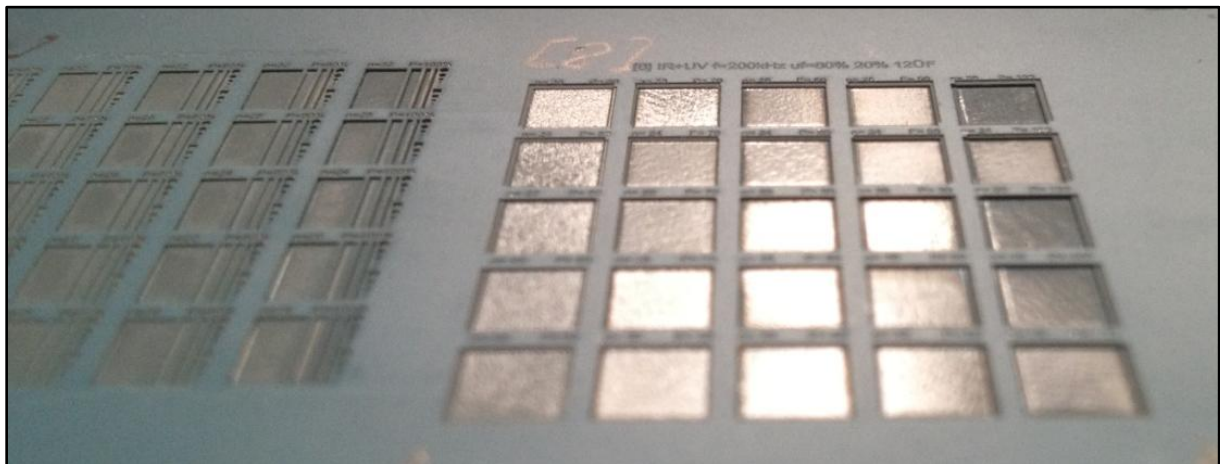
Draufsicht auf die kombiniert bearbeiteten Testfelder der Matrix 22
